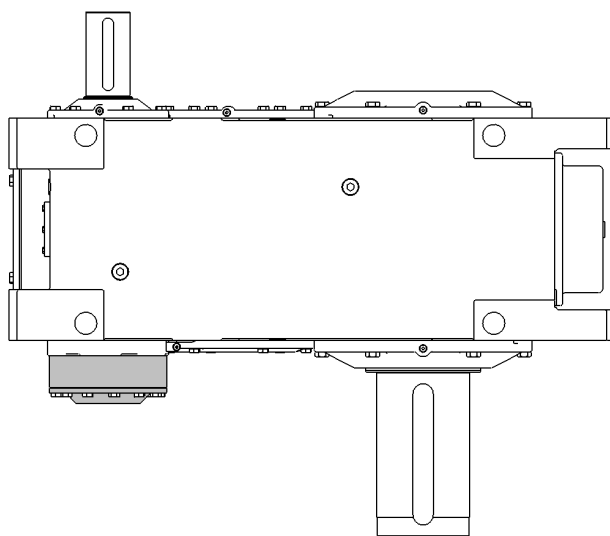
Промышленный редуктор с блокировкой обратного хода
